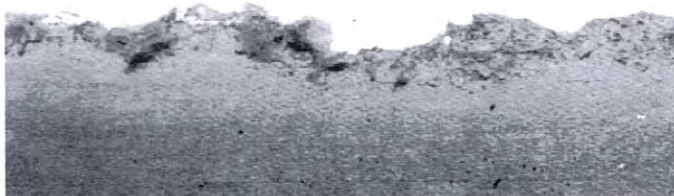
Aspetto di un estruso venuto a contatto in cantiere con una soluzione a base di acido cloridrico (foto tratta dalla pubblicazione CIOA *Difetti dell'alluminio e dell'alluminio anodizzato*)
